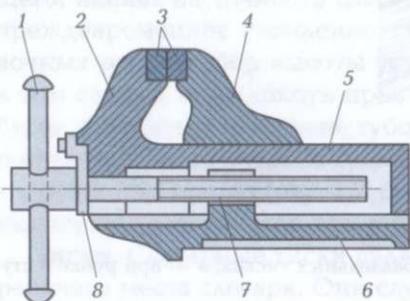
Параллельные неповоротные тиски с ручным приводом:
